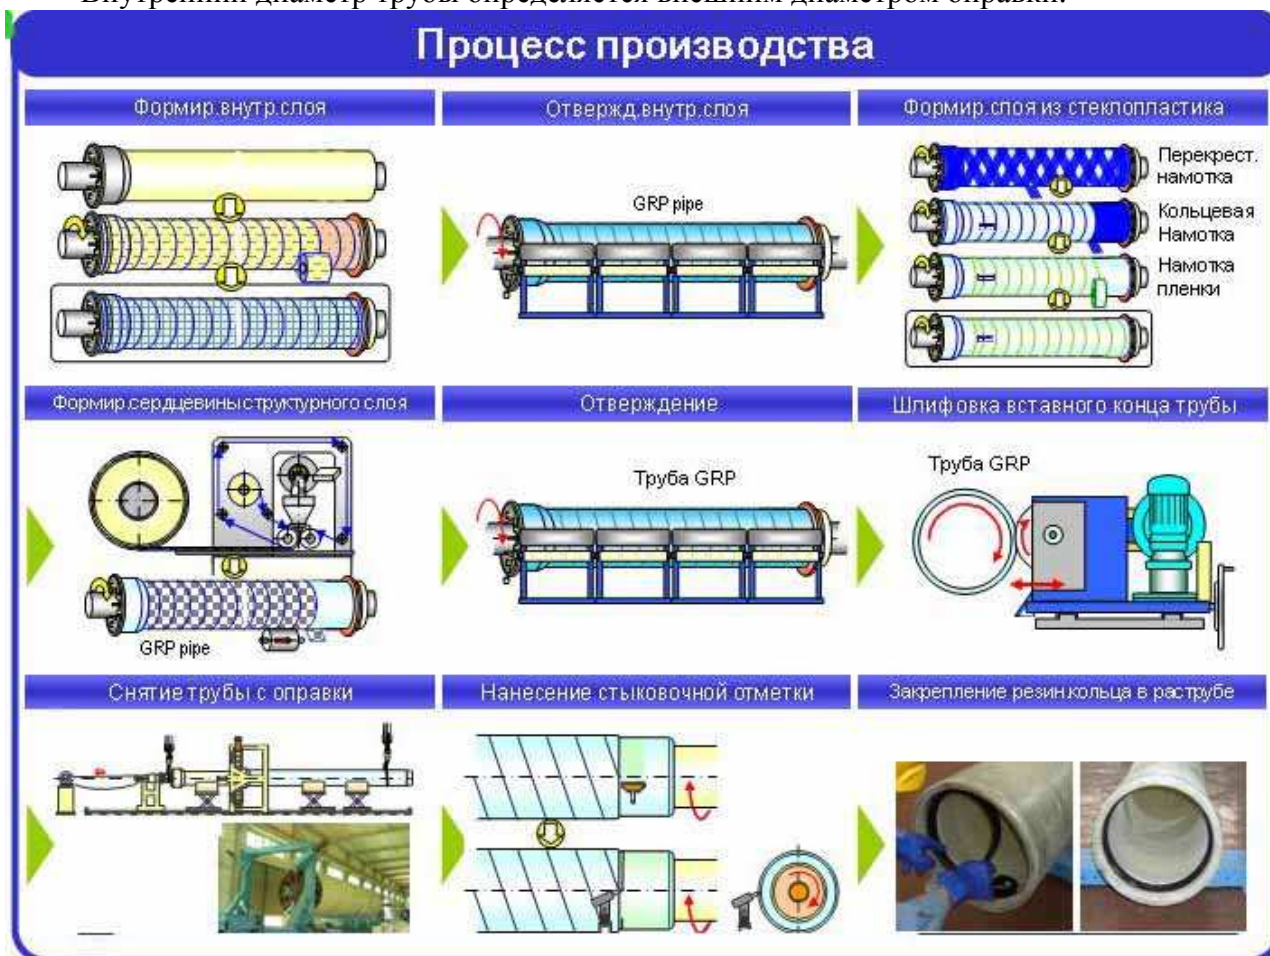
Процесс изготовления стеклопластиковых труб марки Helyx.
